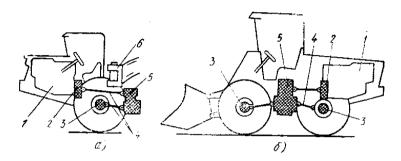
Компоновочные схемы колесных тягачей: а – одноосного; б – двухосного; 1 – двигатель; 2 – сцепление; 3 – ведущие мосты: 4 – карданные валы; 5 – коробка передач; 6 – шарнир сцепного устройства с агрегатируемым оборудованием
